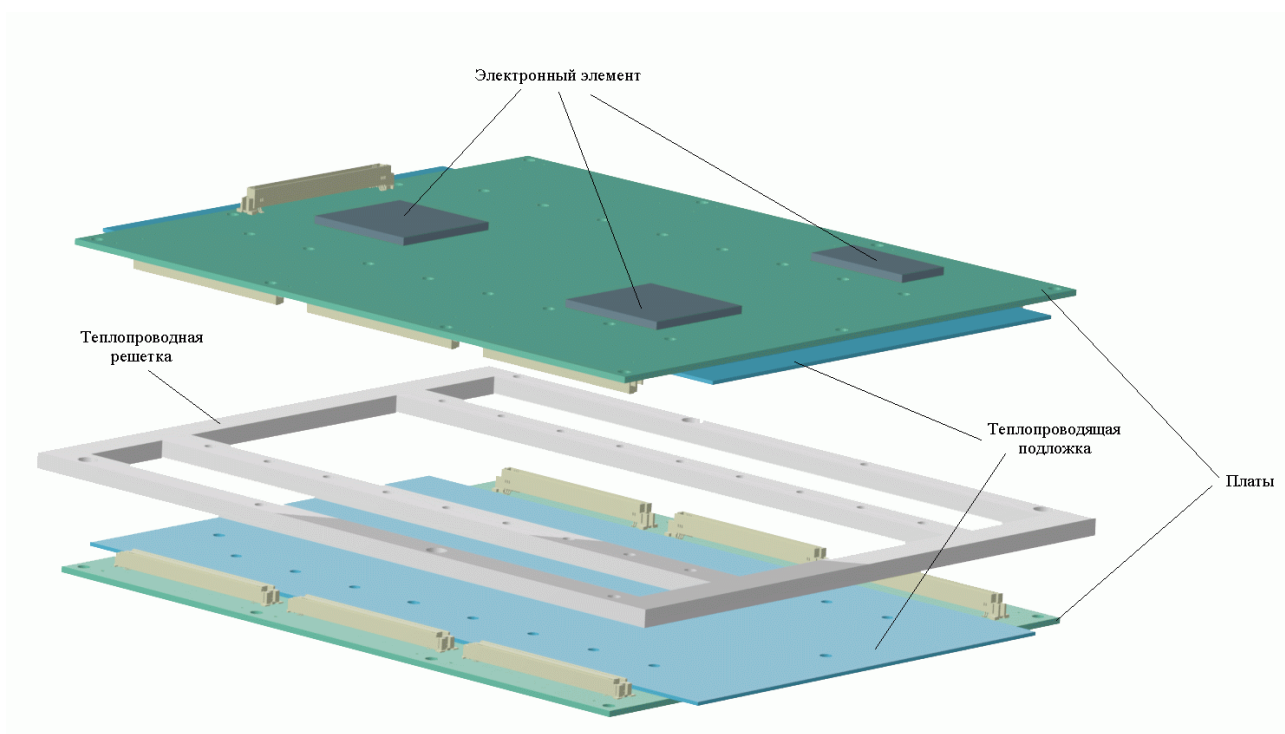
Электронная плата с теплопроводящей подложкой
